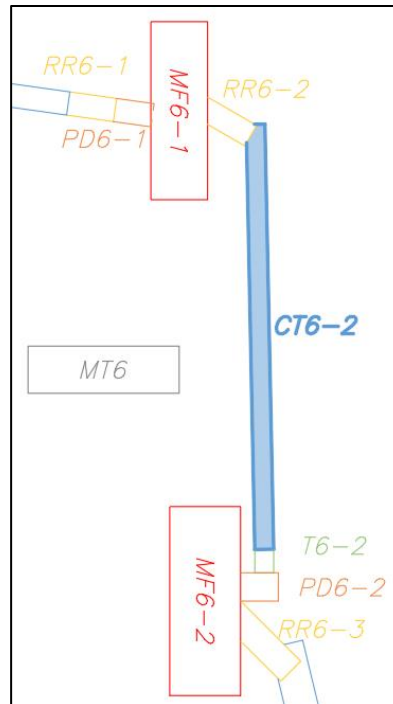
Disposición de la cinta CT6-2 en la planta
